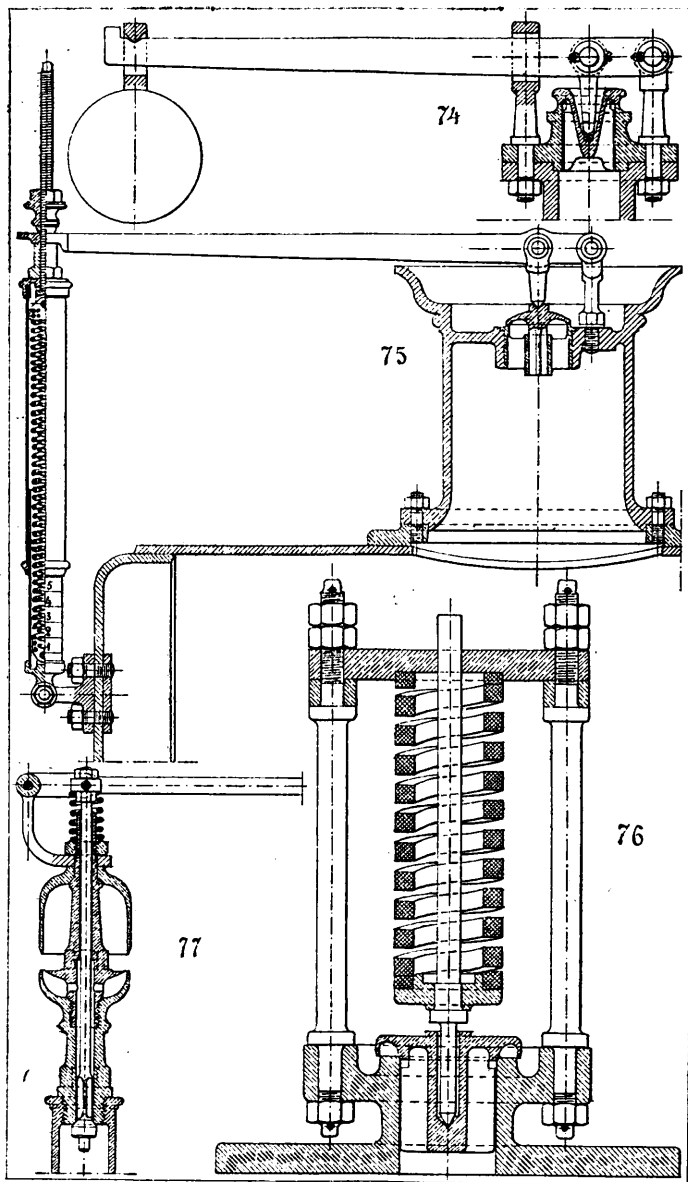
Soupape à levier et à poids. — Fig. 75. Soupape à levier et à ressort. — Fig. 76. Soupape Adams, à charge directe. — Fig. 77. Sifflet.
